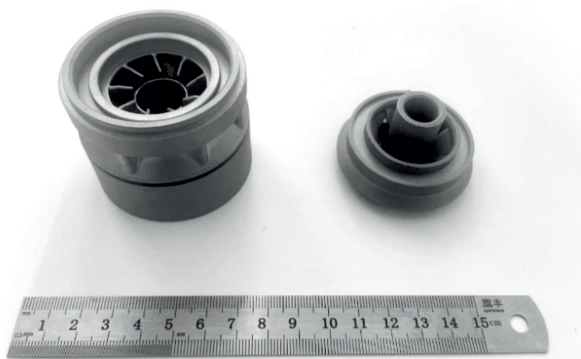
Фото напечатанного рабочего колеса и направляющего аппарата, используемых в ступенях погружных ЭЦН, из порошка нержавеющей стали марки AISI 316L
